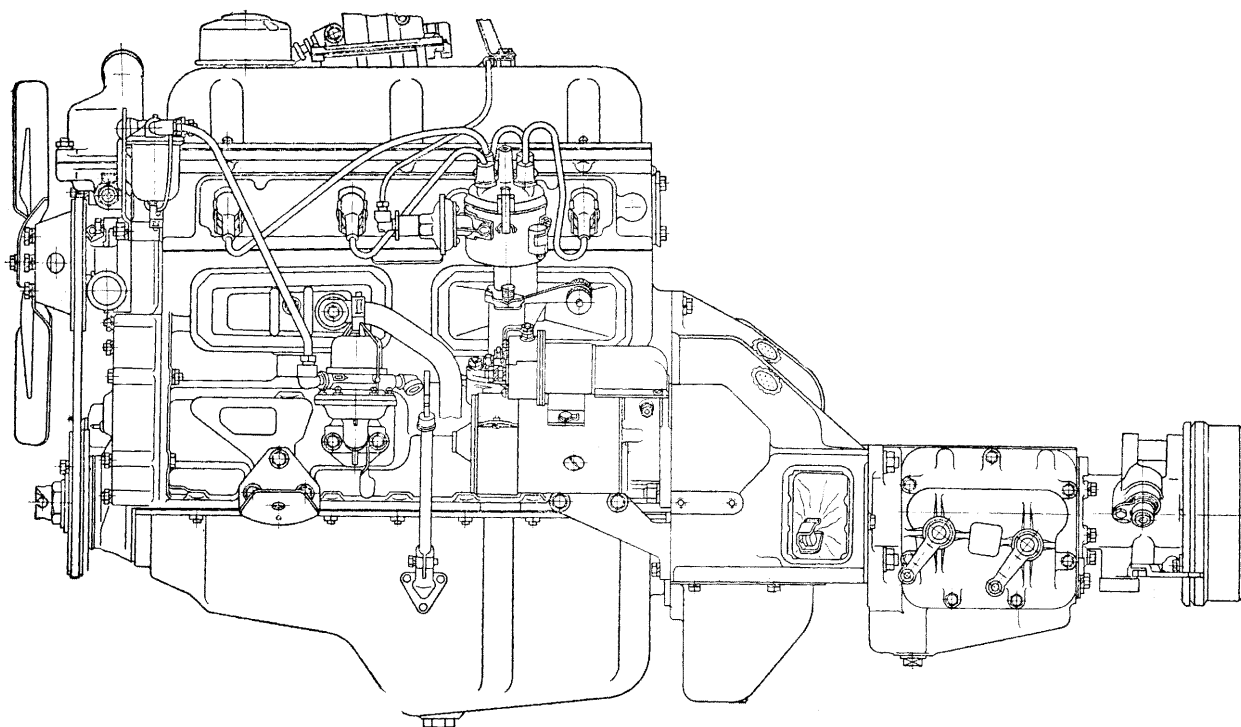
Двигатель со сцеплением и коробкой передач (вид слева)
